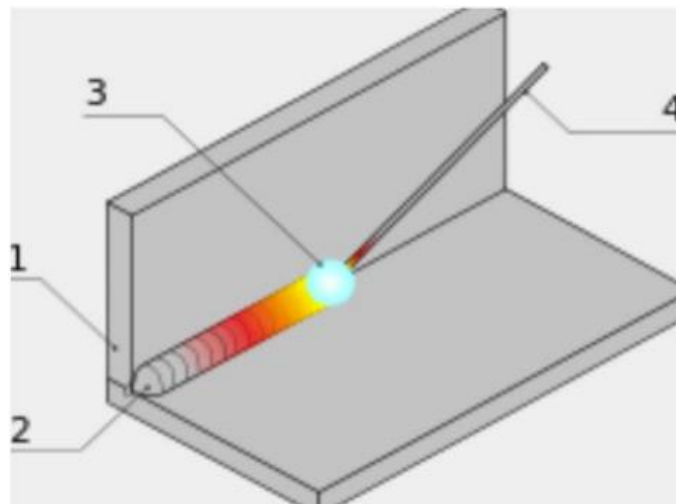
Principios generales de la soldadura. [19]
